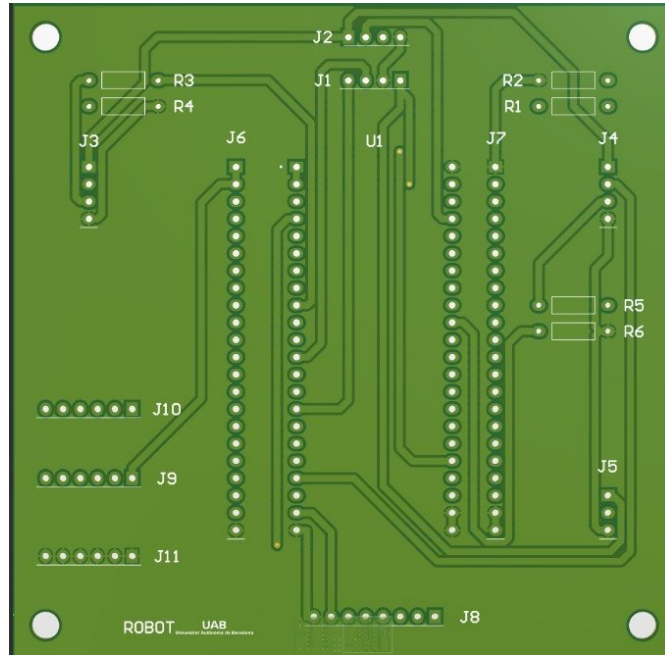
Primera versió de la PCB fabricada per JLCPCB, amb pistes que faltaven i problemes a la màscara de soldadura dels pads.
